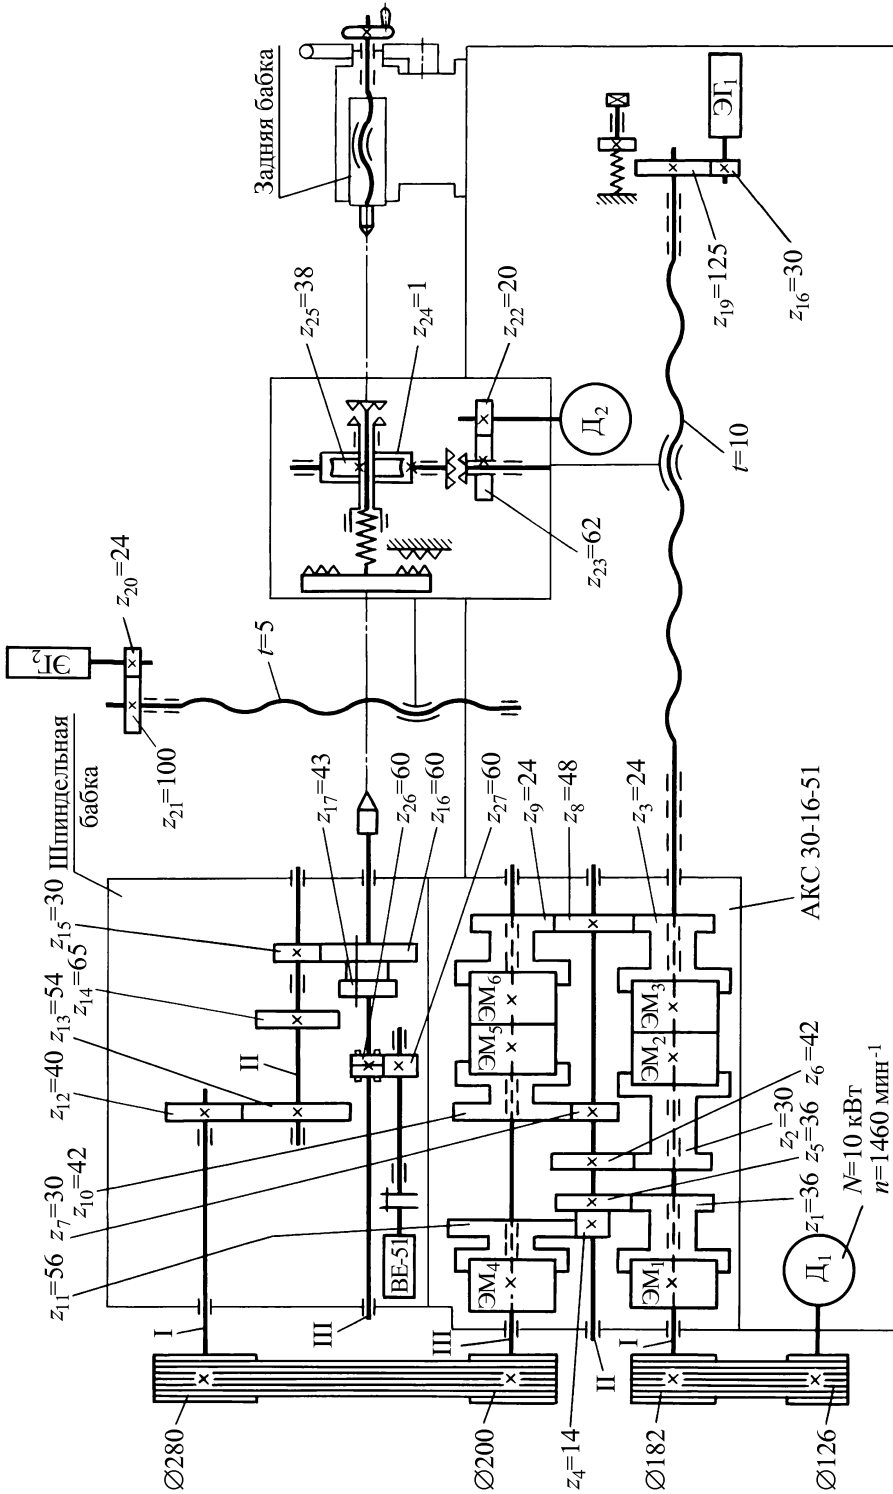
Кинематическая схема станка 16К20Ф3
